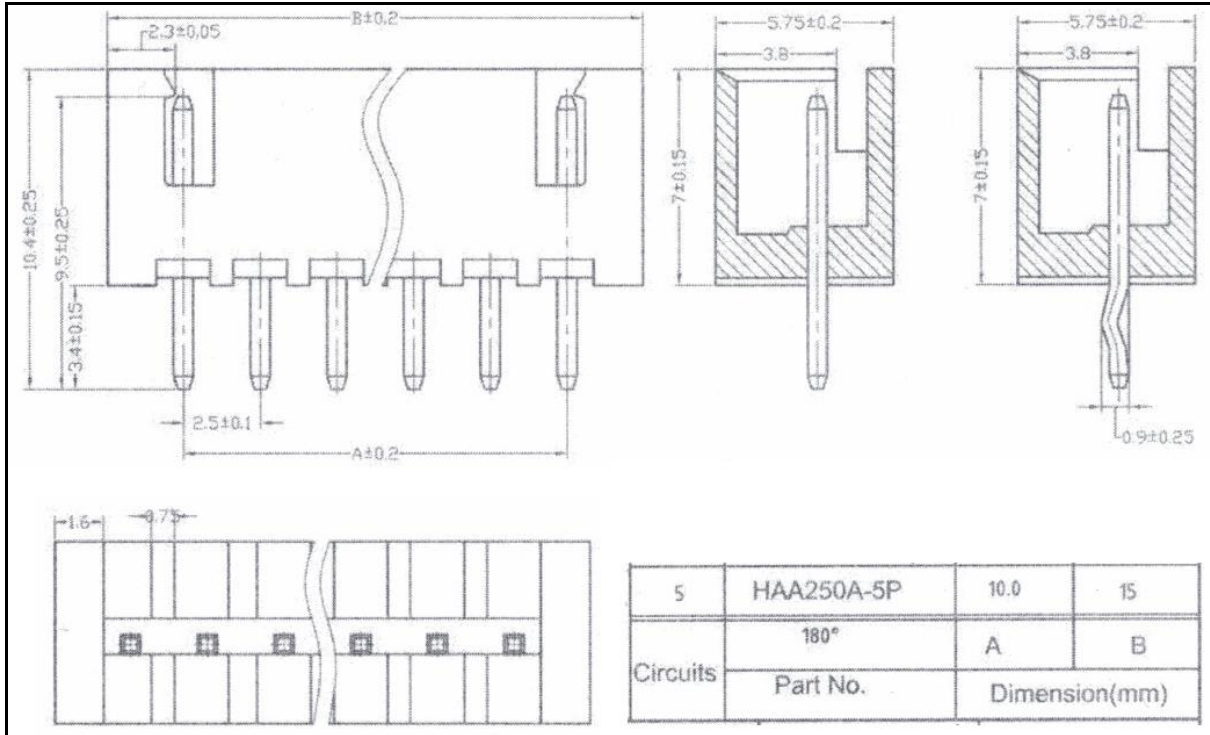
焊接在 PCB 上的插座 J5 尺寸
